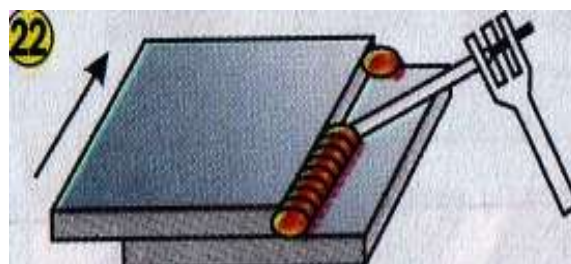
Сварка угловых и тавровых соединений в нижнем положении.
